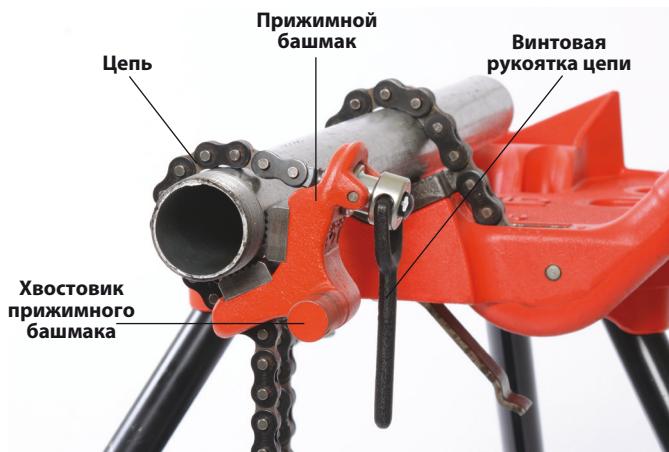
А – Крепление прижимного башмака сложнорычажного ключа на трубе
